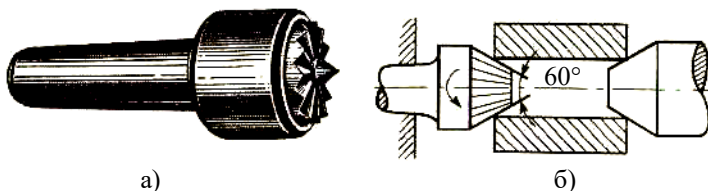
Спеціальні центри із зубами, які обертають заготовку, що обточується:
